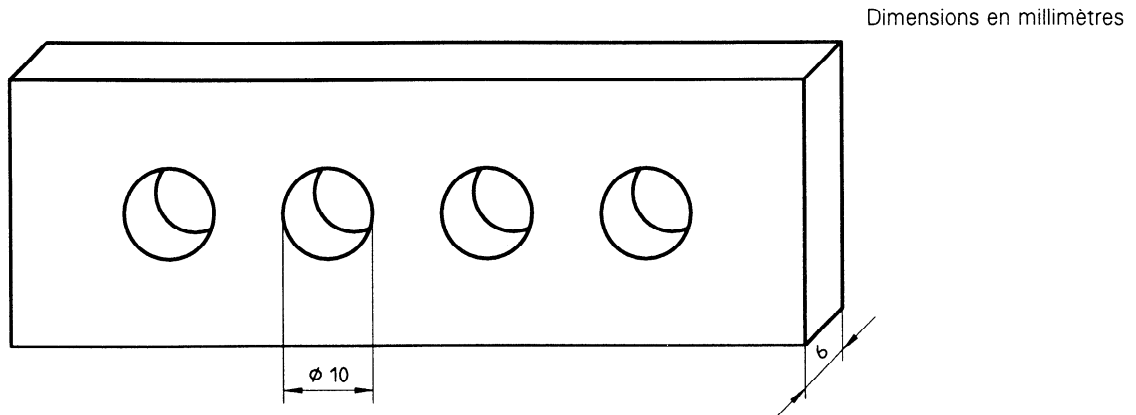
Moule pour éprouvettes soumises à l'essai de fluage
